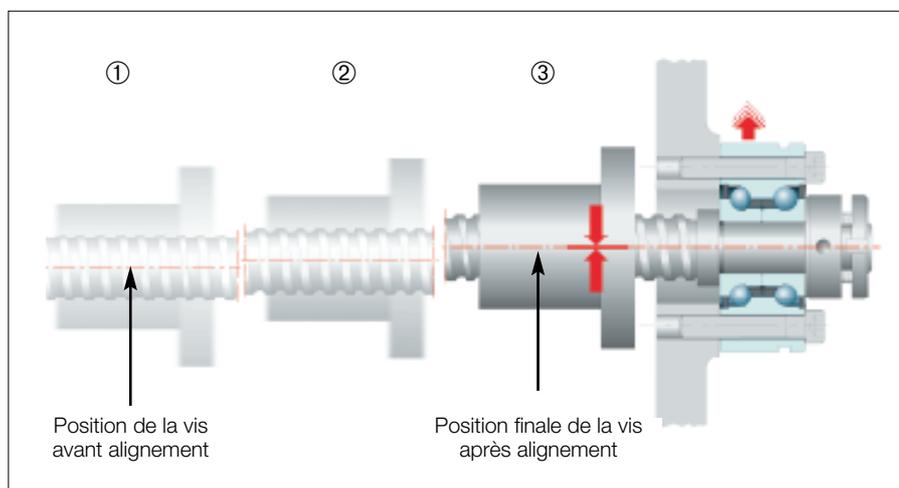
Alignement des roulements par déplacement de l'écrou à billes
